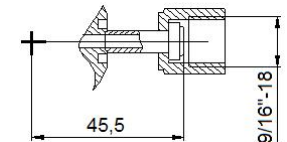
Штуцер (выходной) для торцевого уплотнения Ni шайбой с гайкой с дюймовой резьбой 9/16"-18
